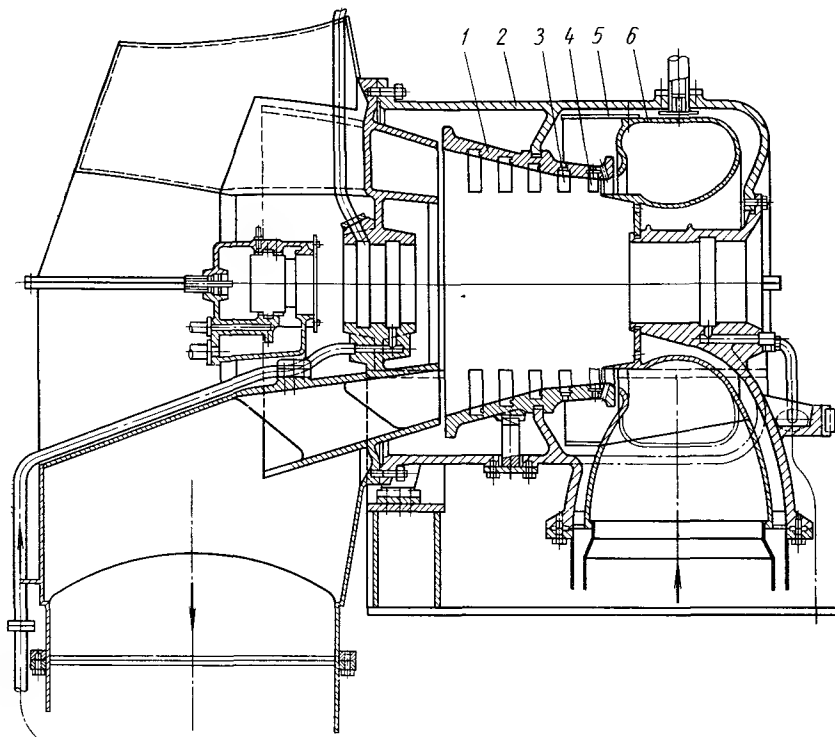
Корпус турбины ГТУ мощностью 7500 квт фирмы Зульцер:
